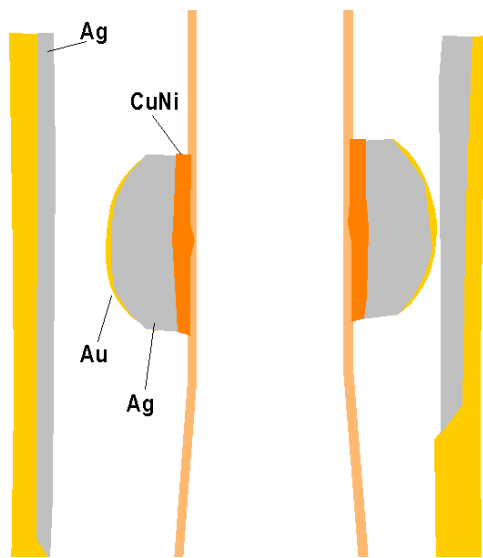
Dreikomponentiger Aufschweißkontakt [63]
